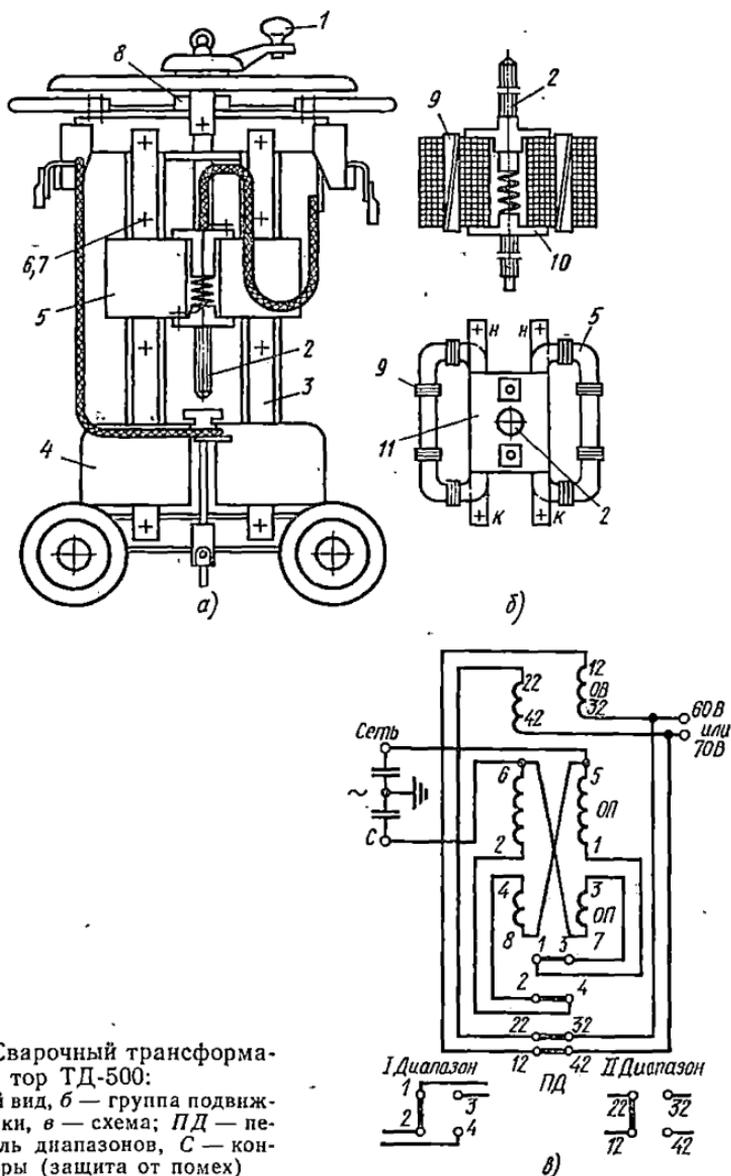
Сварочный трансформатор ТД-500:
